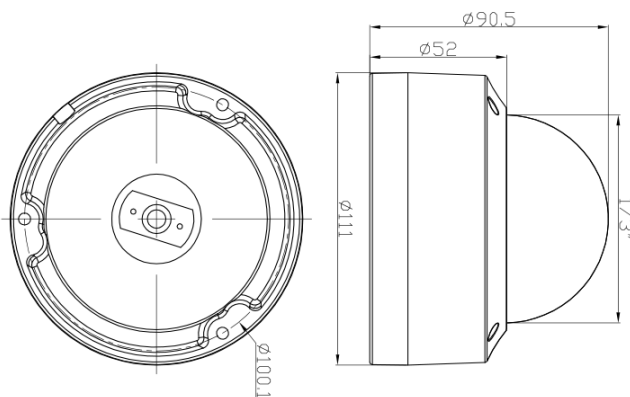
Габаритный чертеж видеокамеры ИВМ-401.
